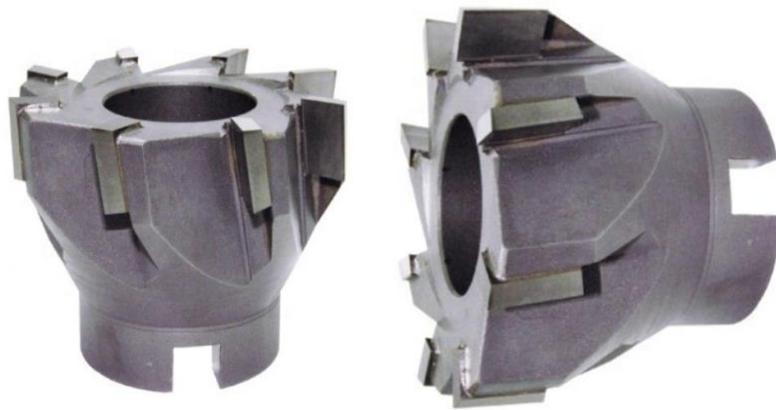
Торцева фреза з напайними пластинами фірми DICTOOLS [13]
